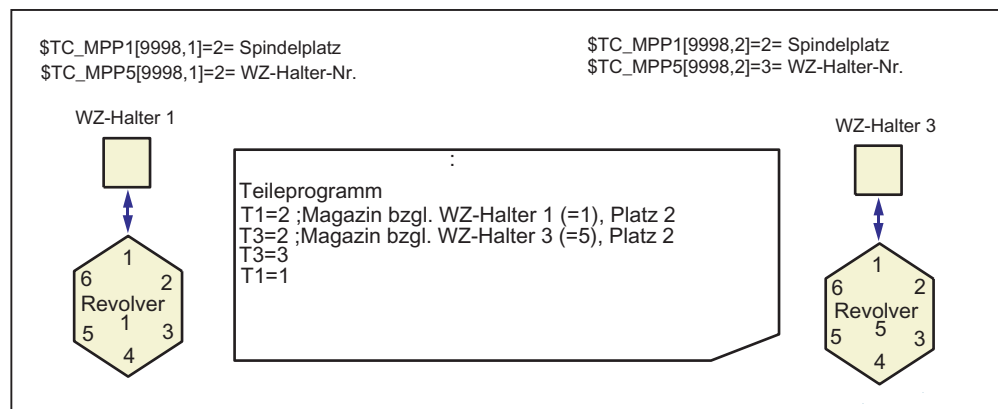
T=Platznummer als Funktion der WZV bei Drehmaschinen
